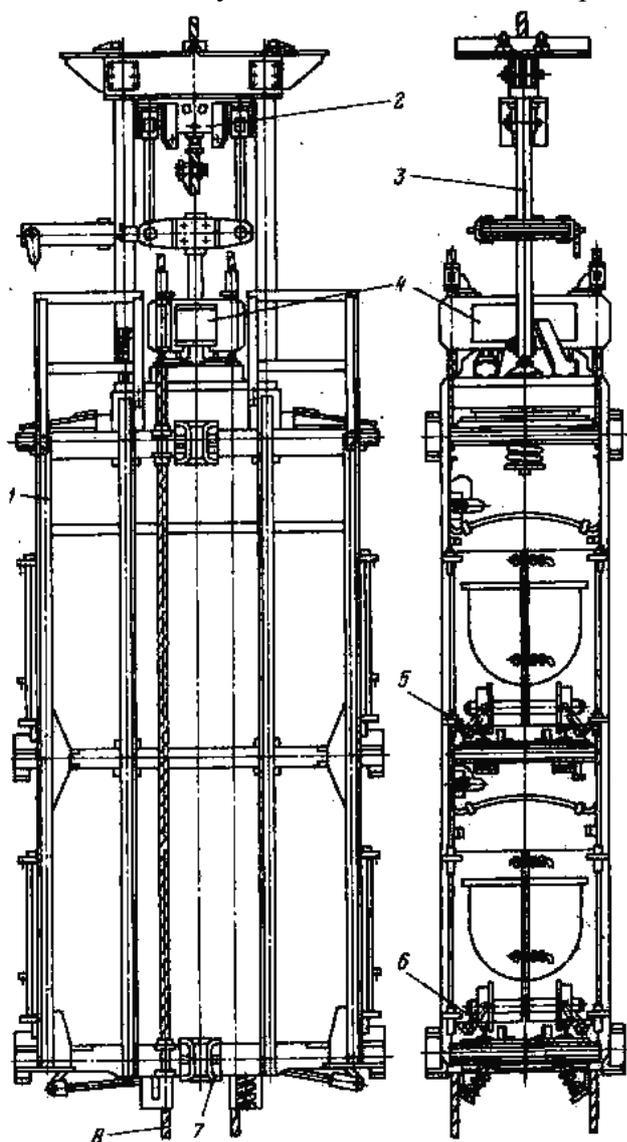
Двухэтажная клеть: 1 – каркас; 2 – прицепное устройство; 3 – подвесное устройство; 4 – парашют; 5 – рельс; 6 – стопорное устройство; 7 – направляющее устройство; 8 – тормозной канат
